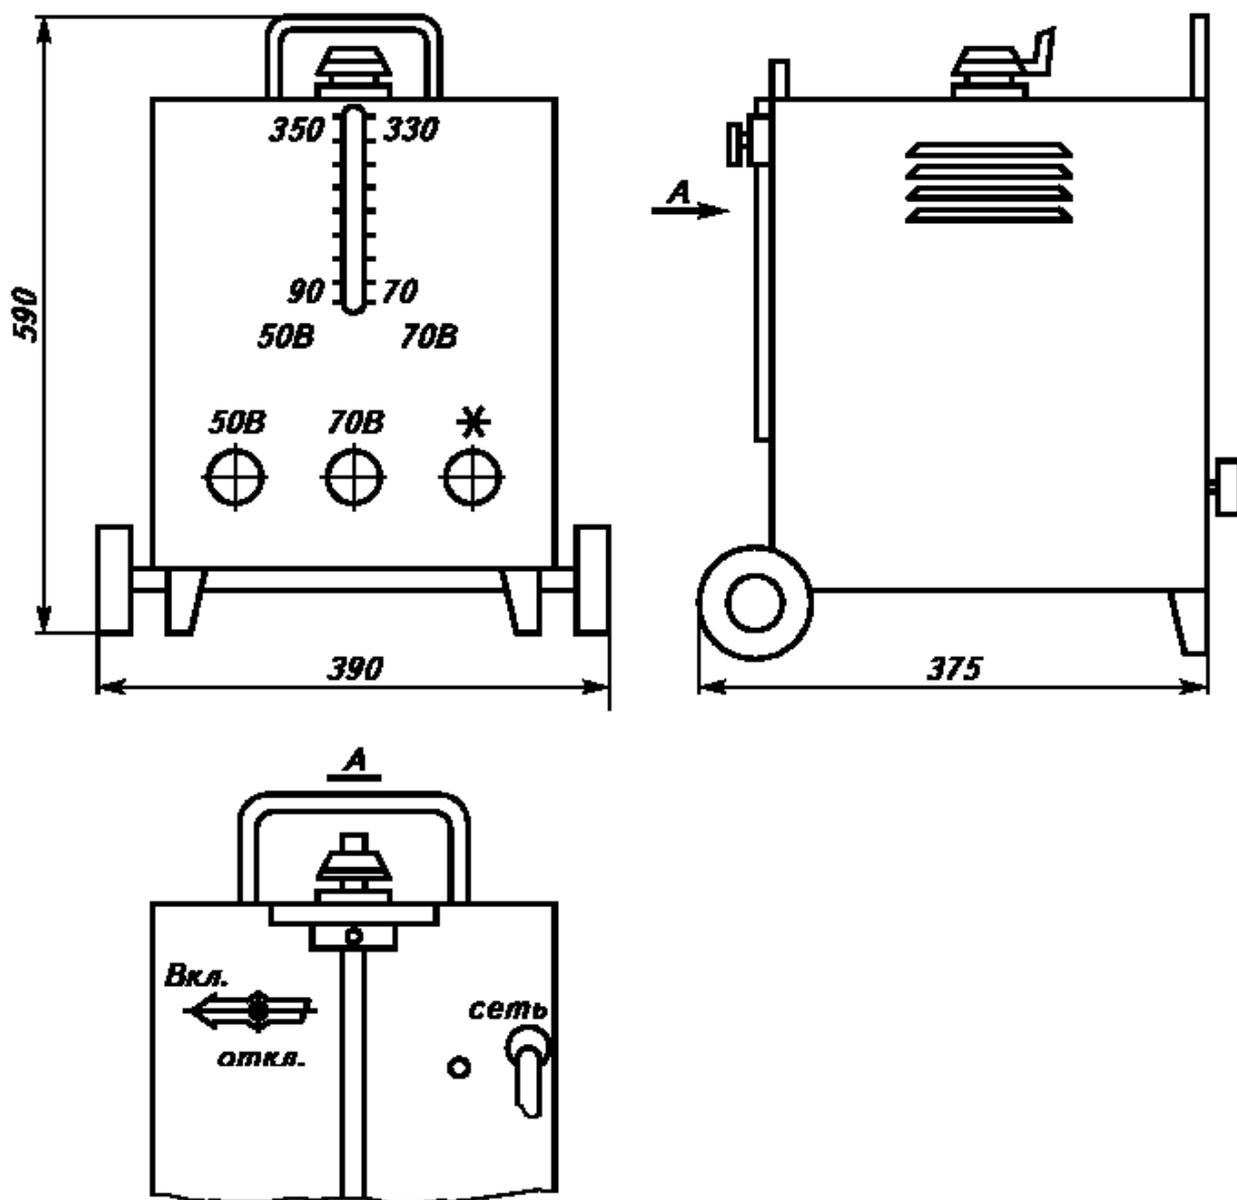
Общий вид и габаритные размеры ТДМ – 300 У2
